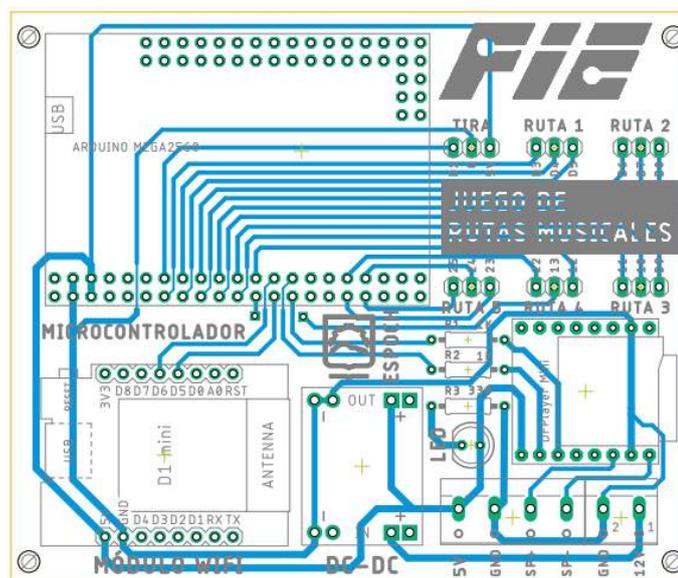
Diseño de la placa PCB del módulo rutas musicales
